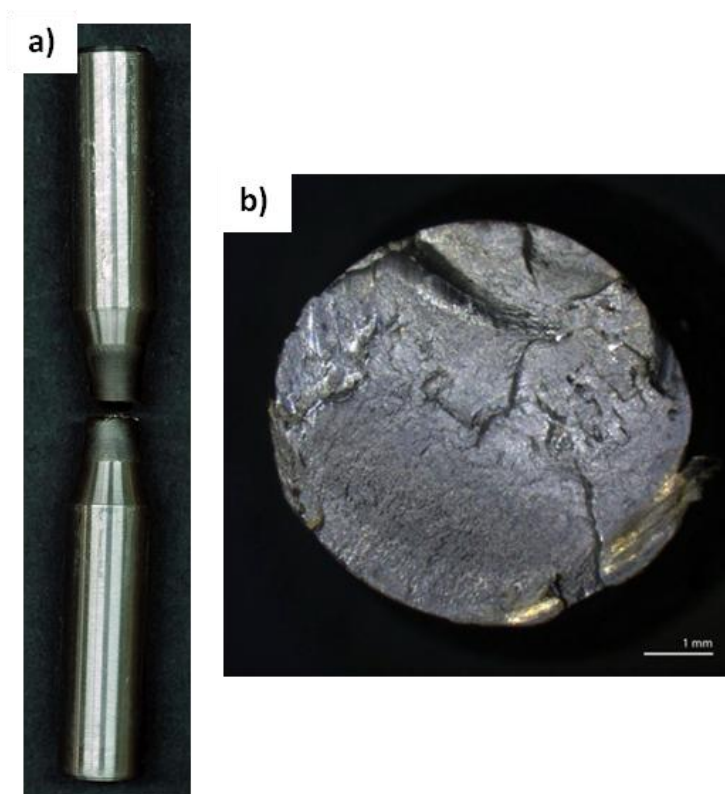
(a) Probeta de fatiga rotativa de 316 LVM procesada con “láser peening” después de ser sometida a tensión de 400 MPa ($N = 88000$). (b) Superficie de fractura por fatiga de la misma probeta.
